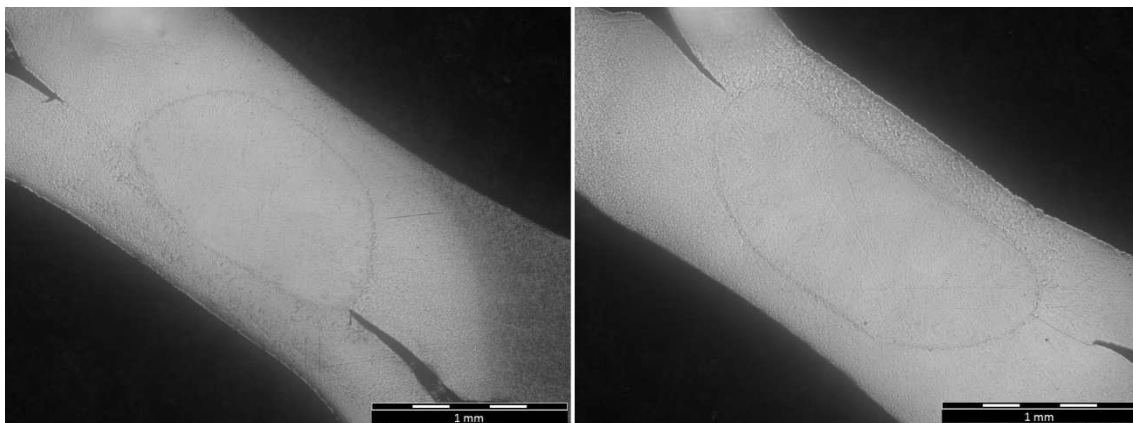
Macrografia das duas lentes de solda do corpo de Prova RCM126.
